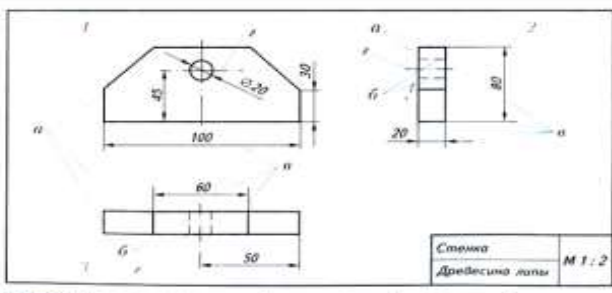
Чертёж детали –стенки: 1 – главный вид; 2 – вид слева; 3 – вид сверху; а – основные линии; б – штриховые линии; в – размерные и выносные линии; г – штрихпунктирные линии.
